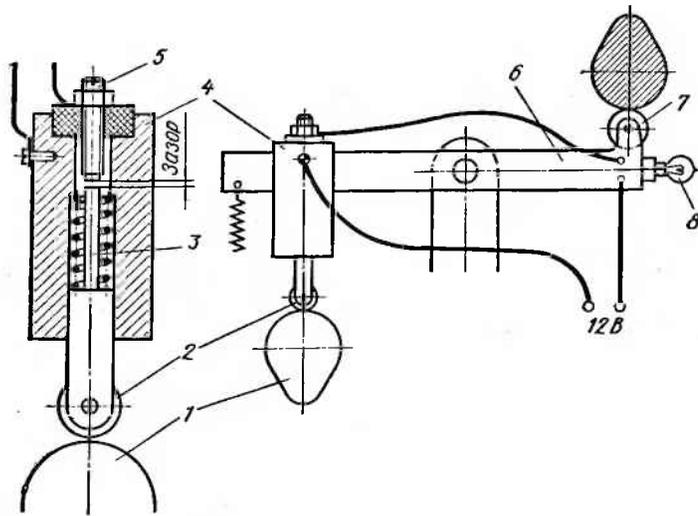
Схема контрольного приспособления для измерения припуска по эксцентрику поковки вала
